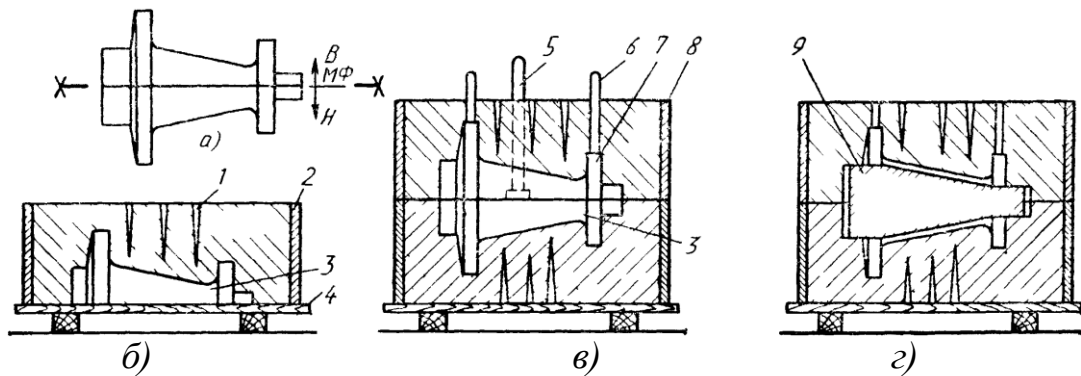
Виготовлення форми у двох опоках за роз'ємною моделлю: а — положення виливка у формі; б — одна з напівформ виливки; в — засоби ливникової системи живлення та інші елементи; г — розташування стрижня в опоці; 1 — вентиляційні канали; 2 — нижня опока; 3 — нижня половина моделі; 4 — модельна плита; 5 — стояк; 6 — випар; 7 — верхня половина моделі; 8 — опока; 9 — стрижень
